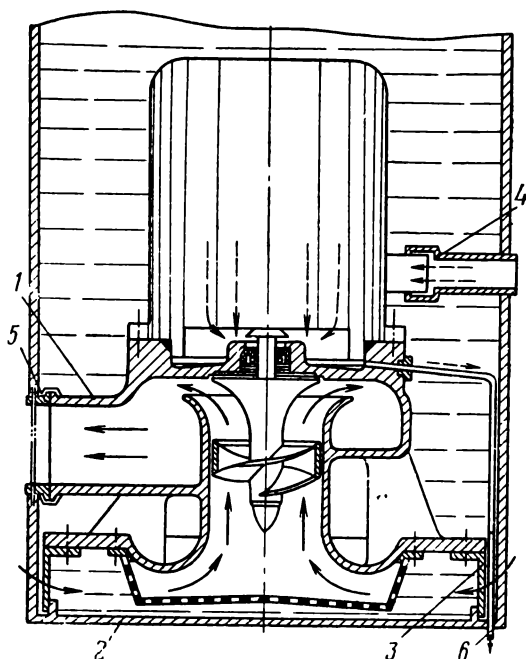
Кессонный ЭЦН для установки внутри бака:
